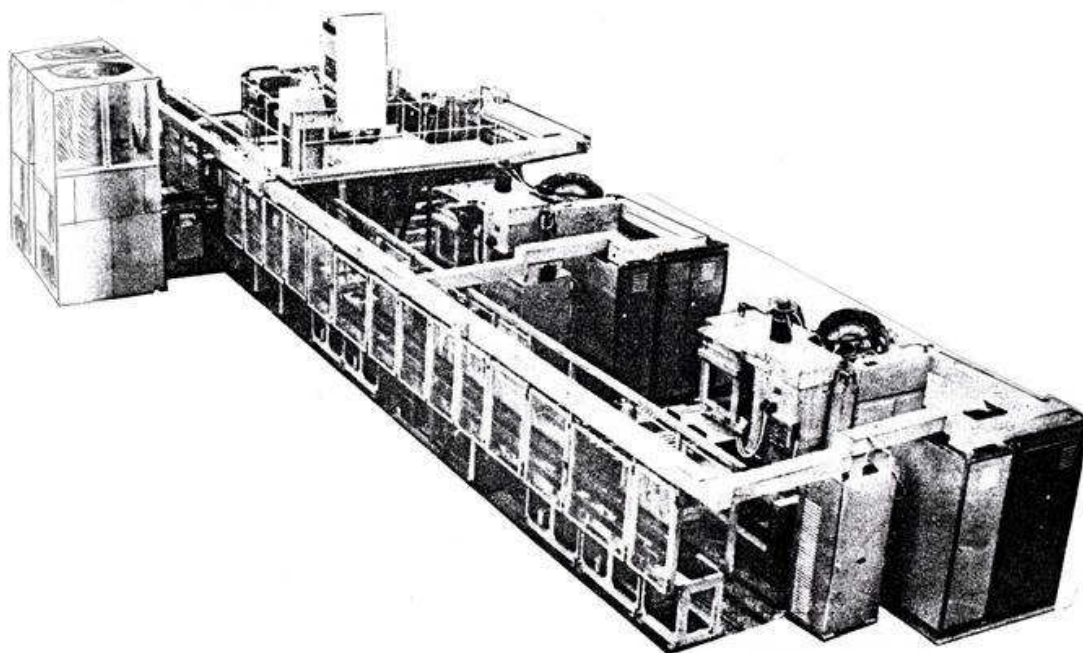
ГАУ типа АСК-0 для обработки корпусных деталей
